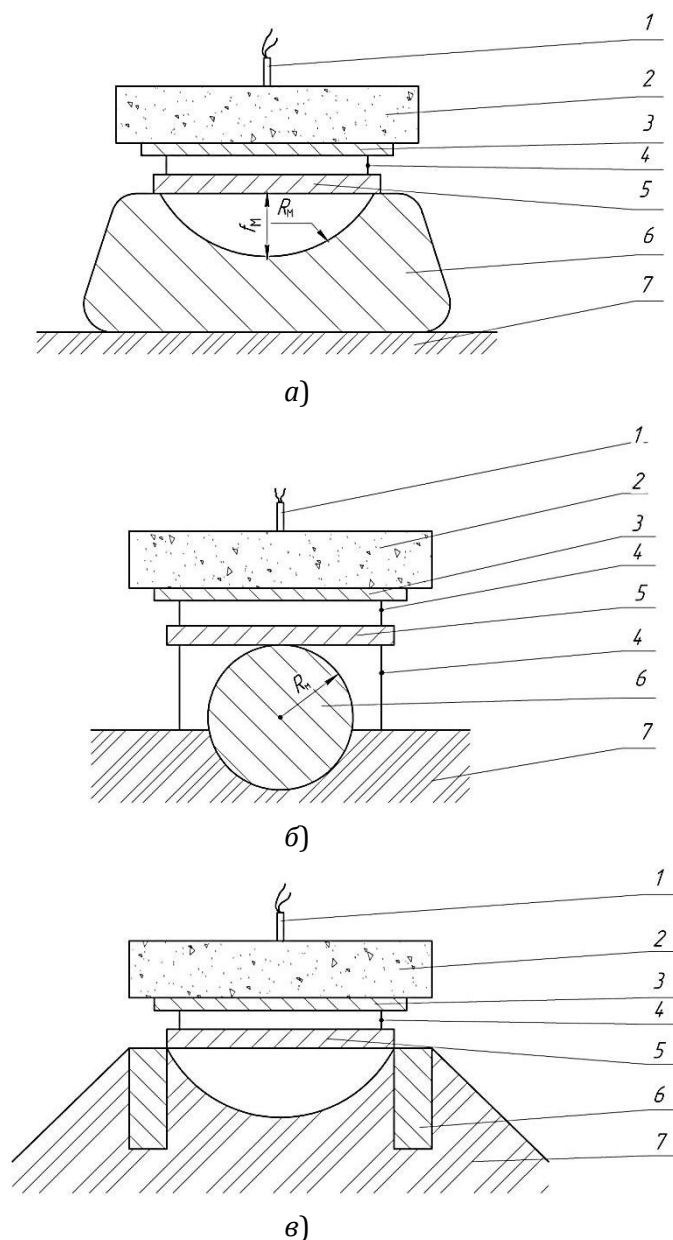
Схемы сварки взрывом с одновременной штамповкой цилиндрических заготовок:
